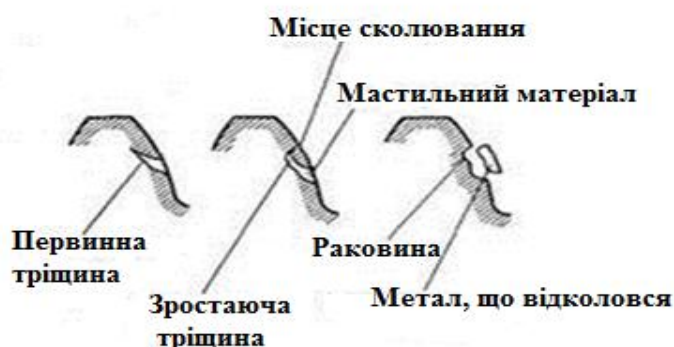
Схема формування тріщини на евольвентній поверхні зубів великогабаритних зубчастих вінців
